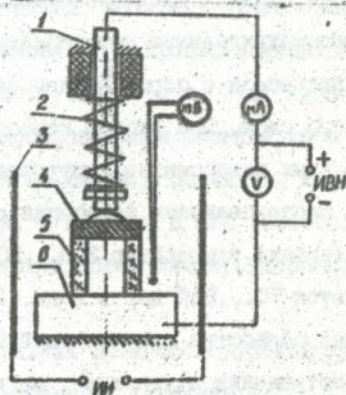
Схема электрохимической сварки: 1 - токоподвод; 2 - пружина; 3 - нагреватель; 4 - кремний; 5 - стекло; 6 - стол; ИН - источник нагрева; ИВН - источник высокого напряжения.
